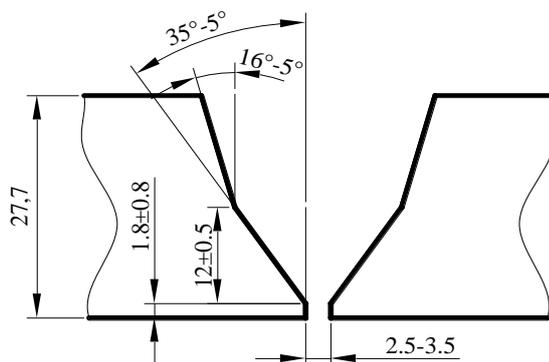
Подготовка кромок труб под сварку
